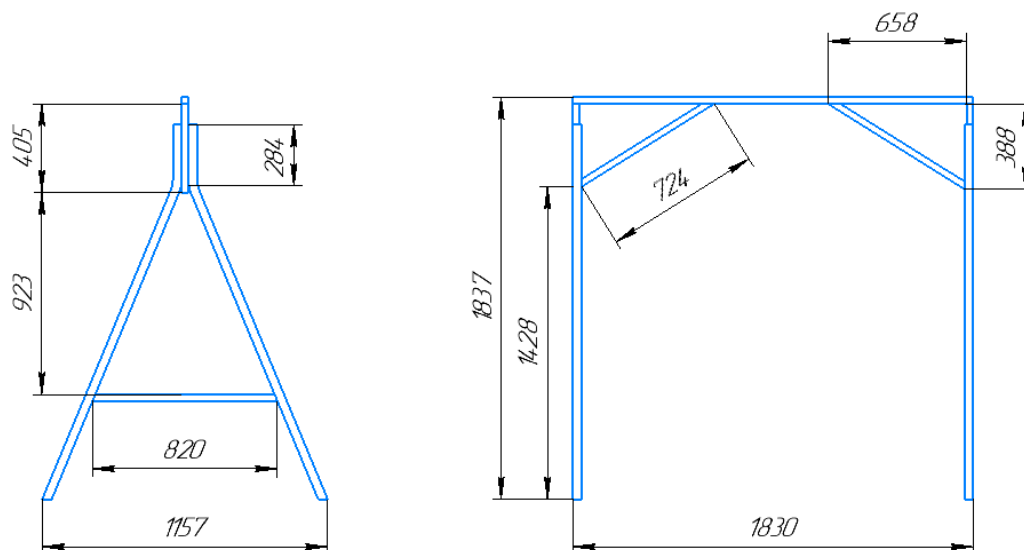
Чертеж каркаса разрабатываемой конструкции
